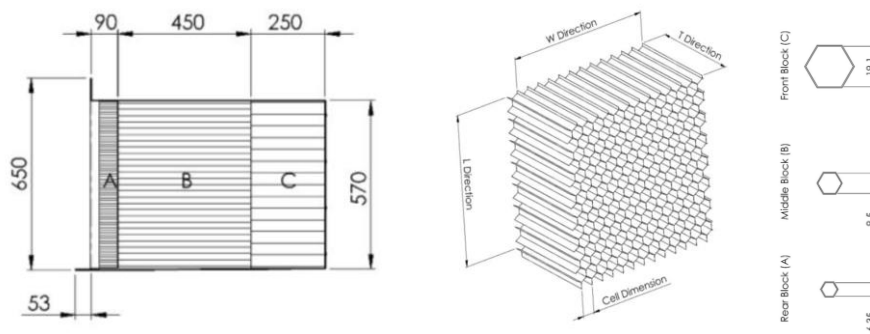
Moving Progressive Deformable Barrier (MPDB) [45] [46]
